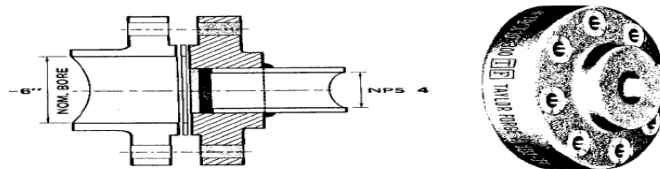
Flange* Jenis WN (*Welding Neck*)
